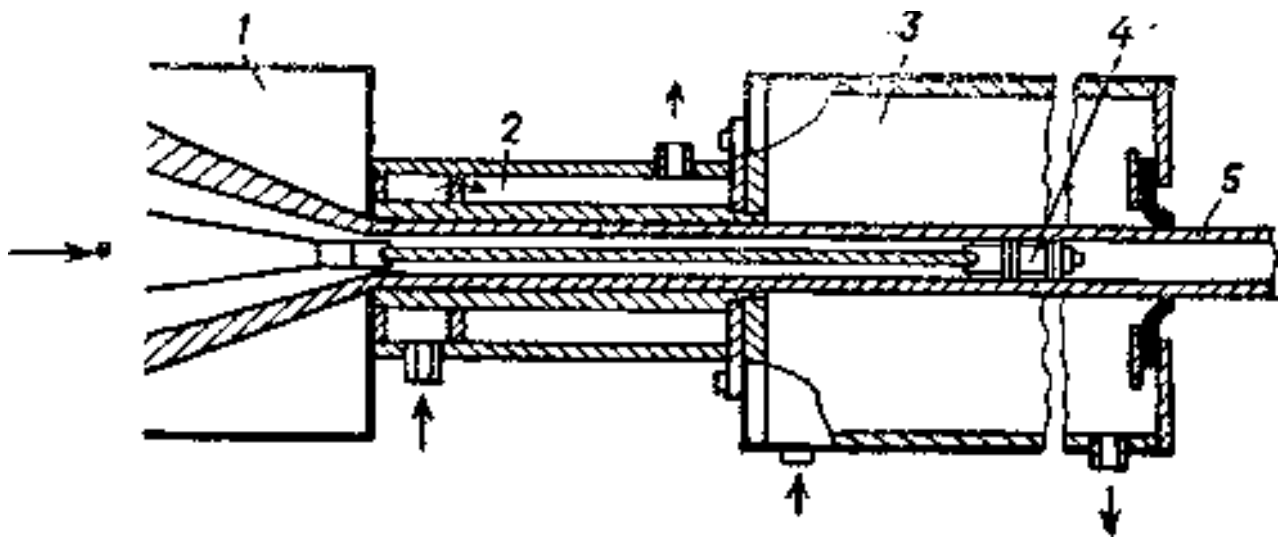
Схема калібрування труби по зовнішньому діаметру:
